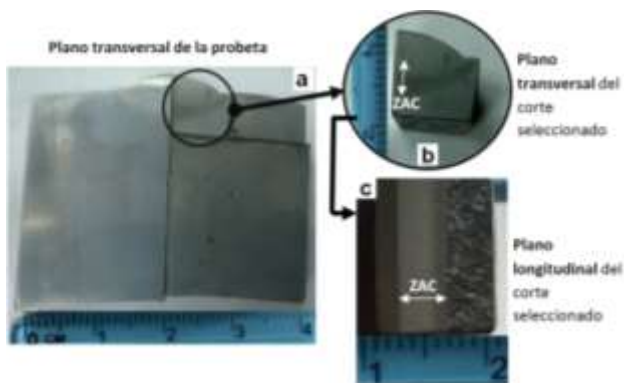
Corte realizado para analizar la probeta. a.- plano transversal. b.- corte seleccionado. c.- plano longitudinal.
